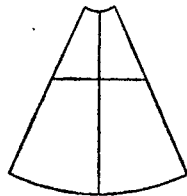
Схема расположения сварных швов лепестка.
